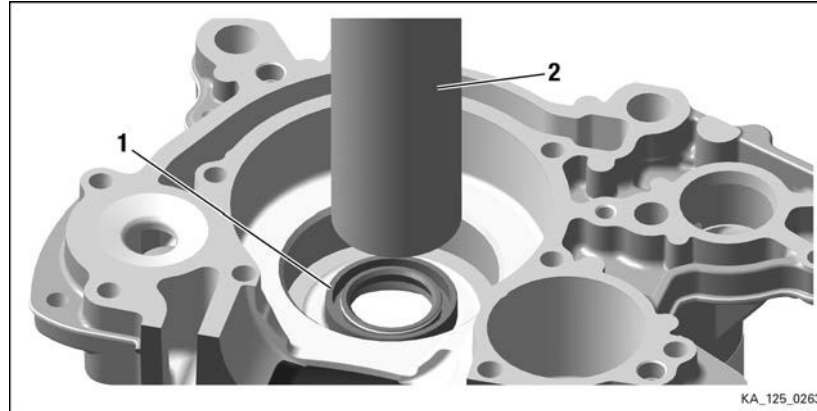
Oil seal installation 油封的安裝治具
